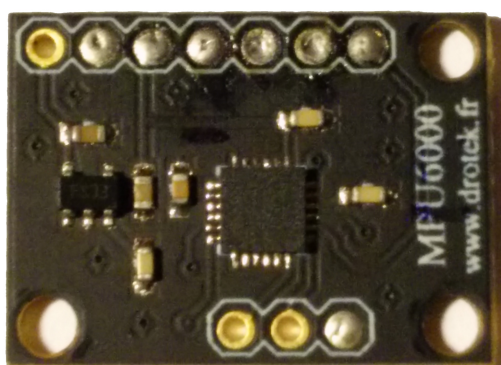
Uma PCB (Printed Circuit Board) de um sensor MPU-6000 (InvenSense, 2015)
